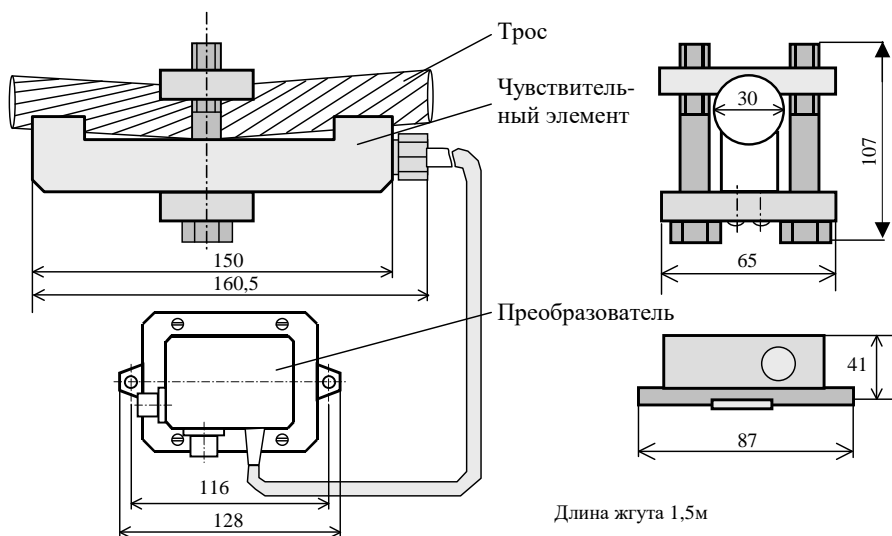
Габаритные и присоединительные размеры ДУКЦ
